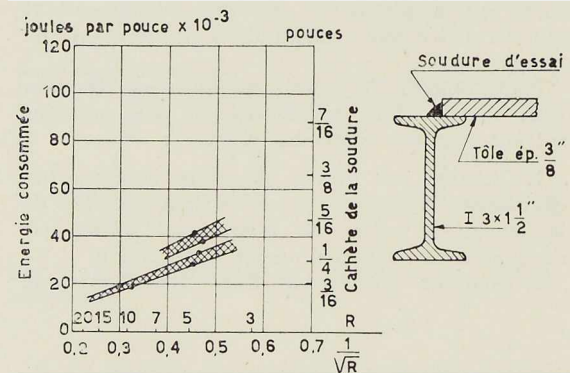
Sévérité thermique d'un joint soudé.
